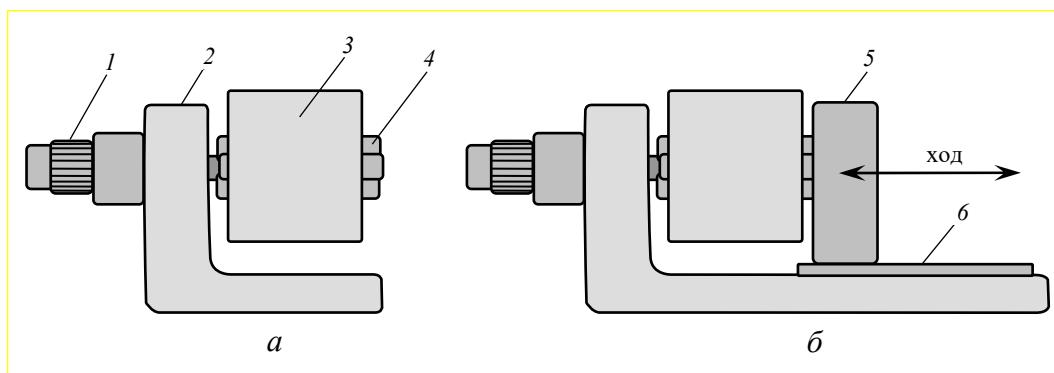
Барабанні моталки : а - Консольна; б - 2-опорна(1 - Мотор-редуктор; 2 - Корпус; 3 - бант; 4 - барабан; 5 - Відвідна опора; 6 - Напрямні)
